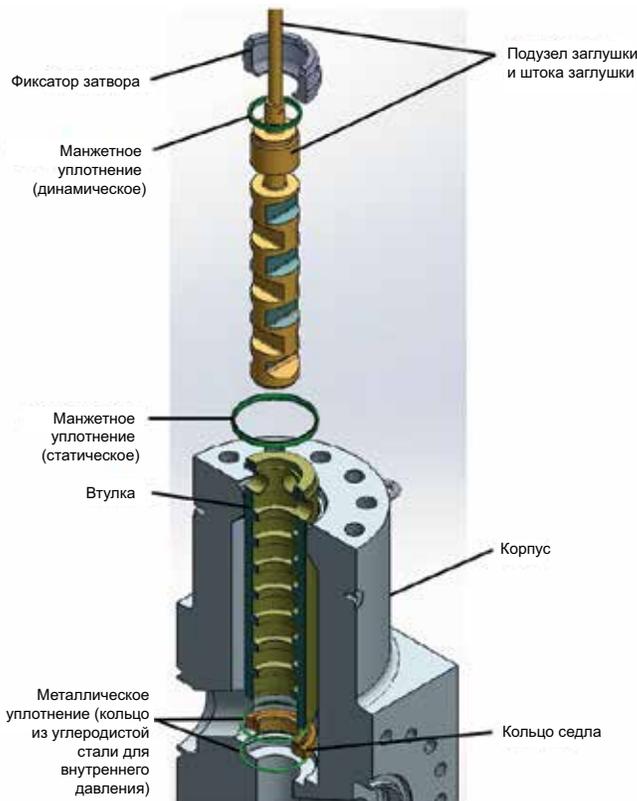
Покомпонентный вид затвора в сборе - Установка кольца седла и втулки (сбалансированный, от 1,5 до 6")
